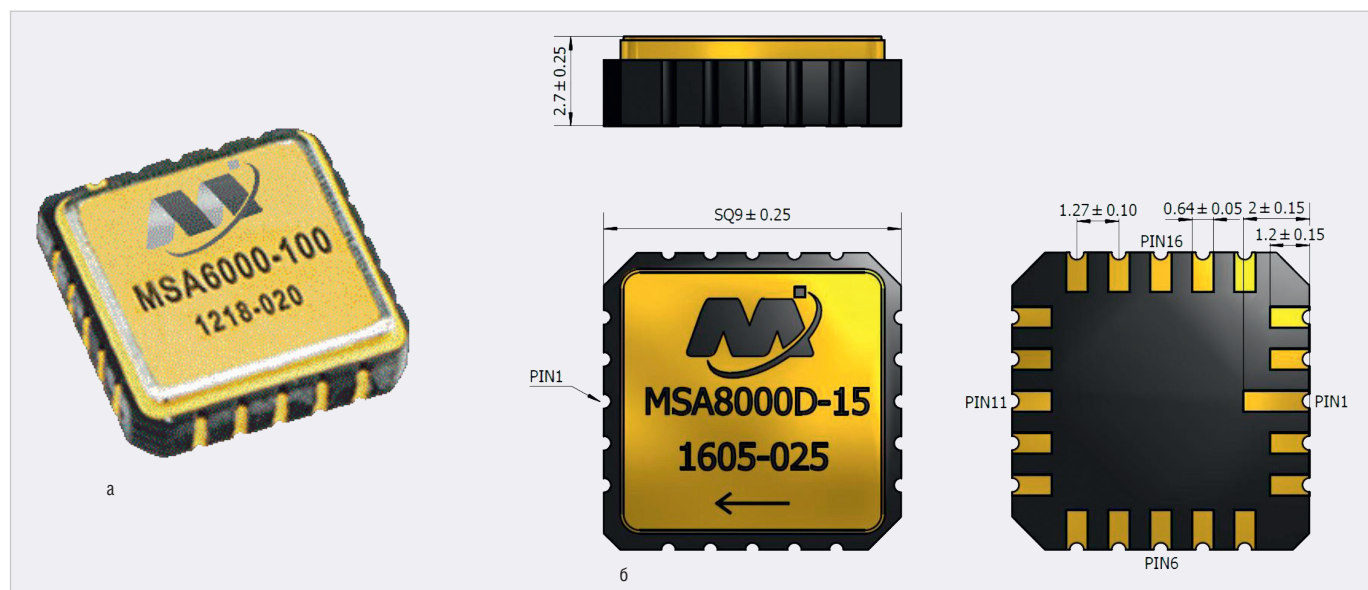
ИМС акселерометров: а) внешний вид; б) габаритные размеры
